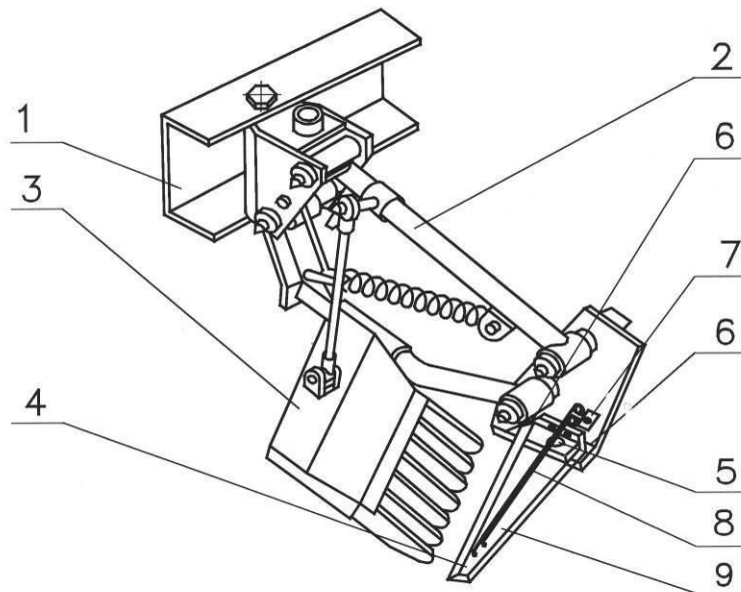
Конструктивна схема гичкозрізувального пристрою з підпружиненим ножем: 1 – рама; 2 – паралелограмна підвіска; 3 – гребінчастий копір; 4 – ніж; 5 – вісь обертання; 6 – упори; 7 – пластинка; 8 – пружина; 9 – ніж
